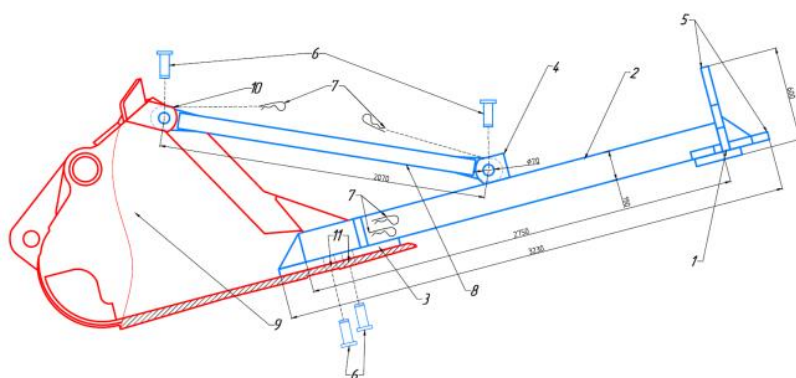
Монтаж ОКН на ковш погрузочно-доставочной машины SANDVIK LH307. 1 – рабочий орган; 2 - стрела; 3 – опорная плита; 4 – проушина для крепления распорной штанги; 5 – перья рабочего органа; 6 – крепежные пальцы; 7 – фиксирующие шпильки; 8 – распорная штанга; 9 – ковш погрузочнодоставочной машины в разрезе; 10 – проушина ковша ПДМ для крепления распорной штанги ОКН; 11 – отверстия в ковше ПДМ для крепления ОКН
